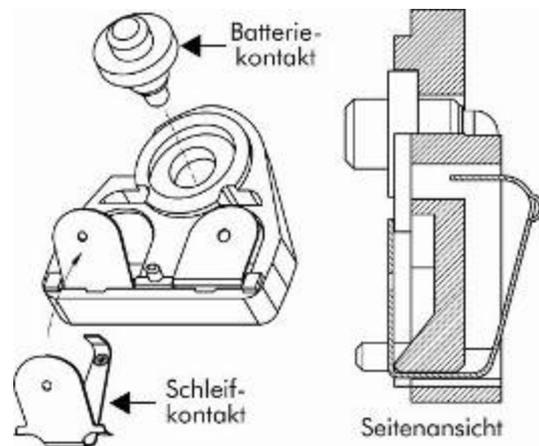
Skizze Federbügelkontakt in gemischter Technologie
